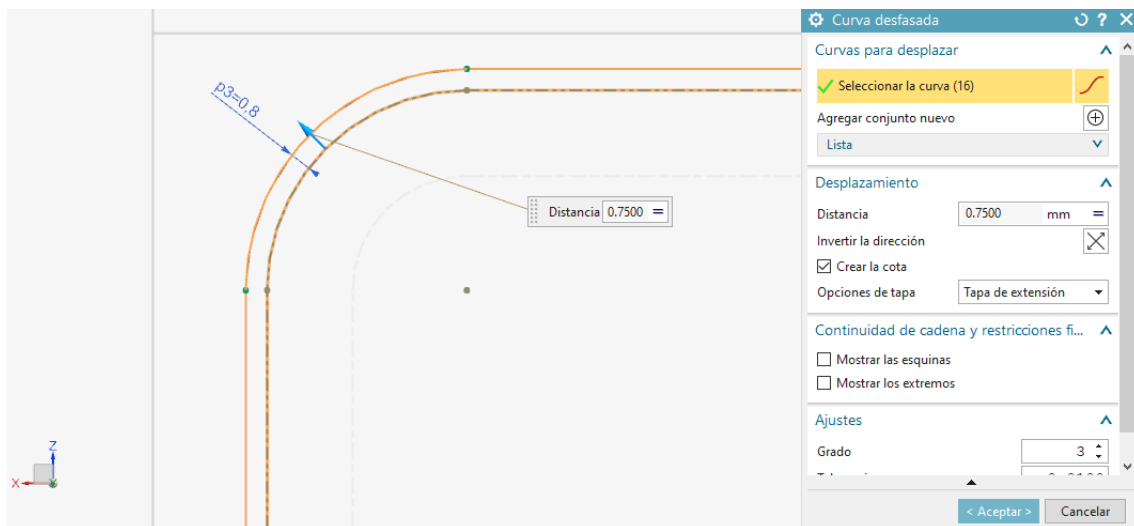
Croquis con sobredimensionado para materiales por corte láser / Fuente: Propia
